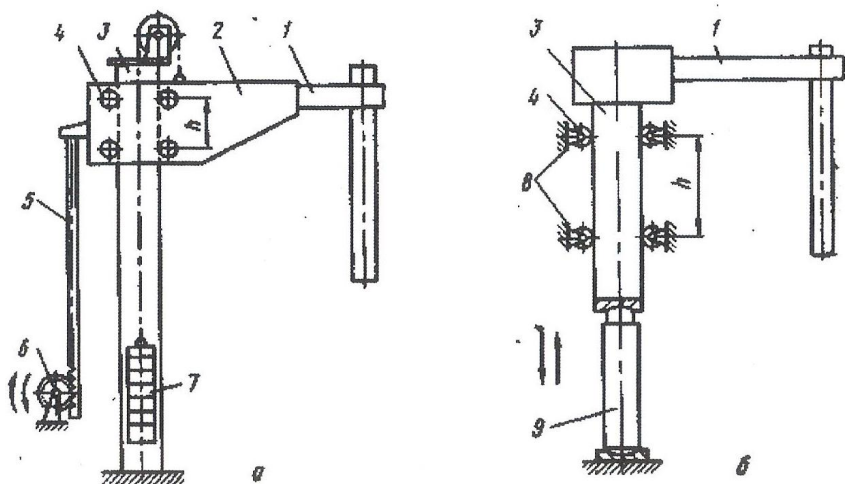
Схема несучих конструкцій с кареткою (а)
